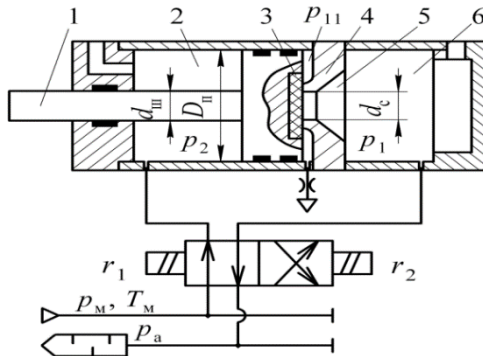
Схема ударного пневмоагрегата (базова)
